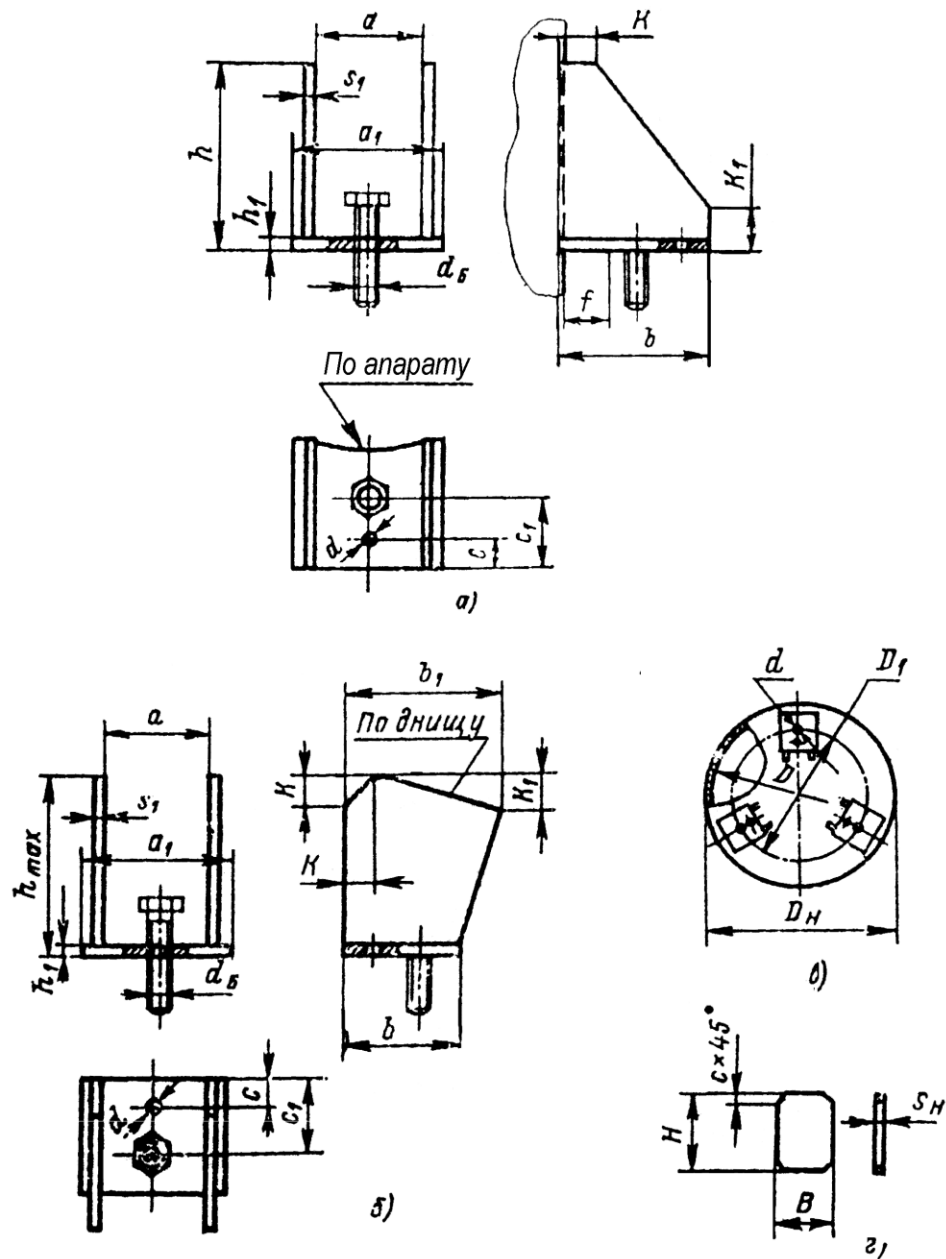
Конструкції стандартних опор (лап і стійок) для сталевих зварних вертикальних циліндричних апаратів: а - лапи; б - стійки; в - схема розташування опор на днище апарату; г - накладний лист
